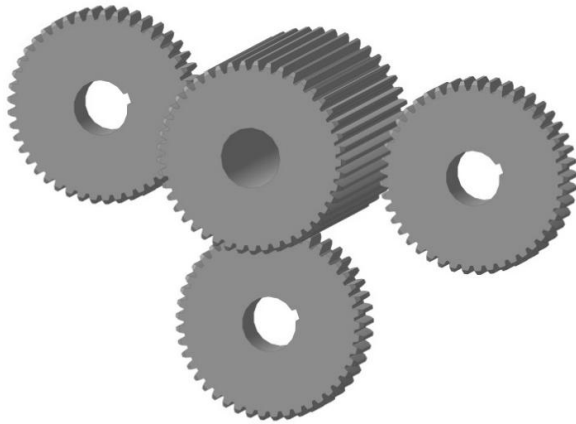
Схема накочування зубчастими роликками зубчастого профілю
